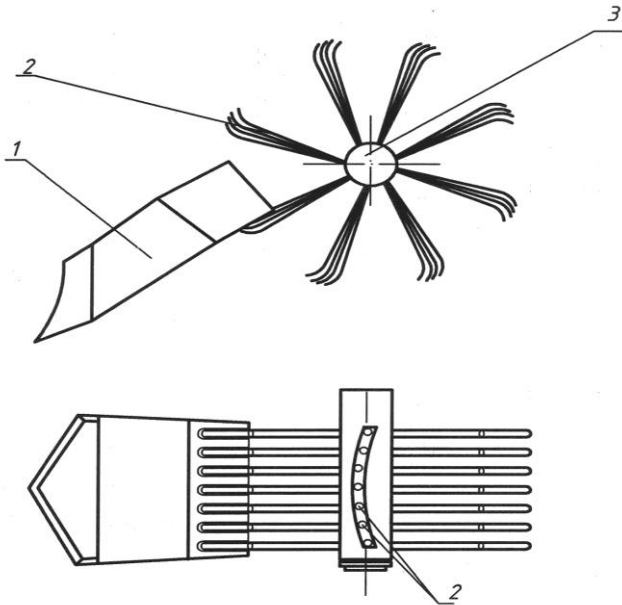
Підкопувально-сепаруючий пристрій роторного картоплекапача: 1 – підкопувальний леміш; 2 – лопаті; 3 – лопатевий вал
